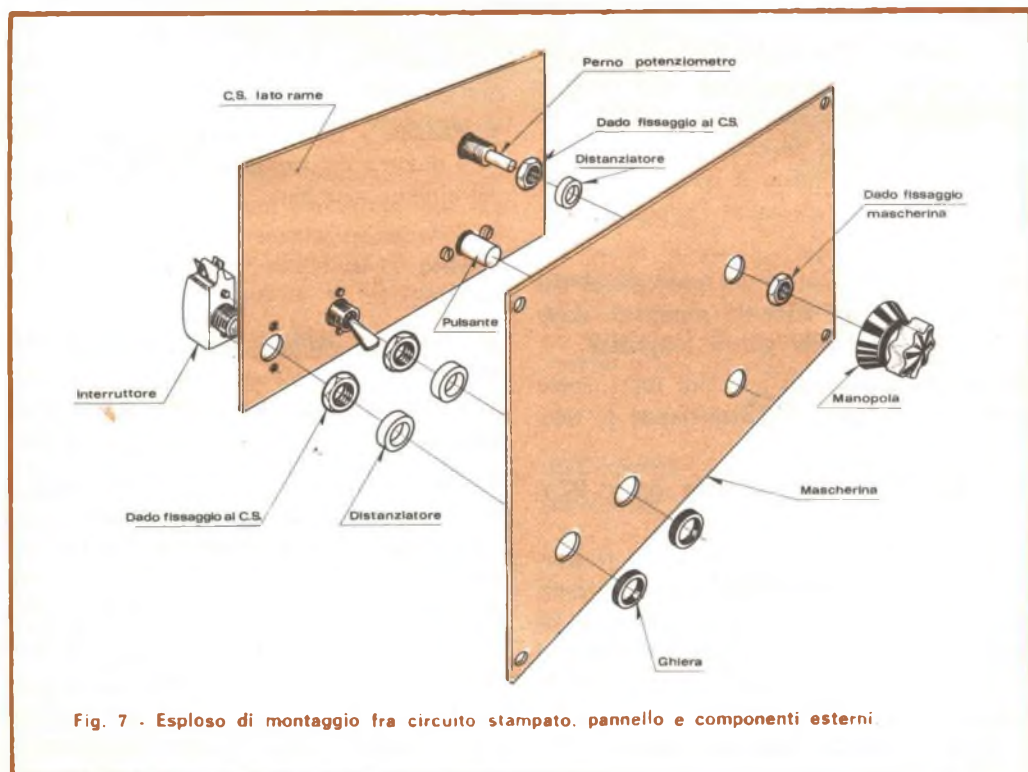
Esploso di montaggio fra circuito stampato, pannello e componenti esterni.
